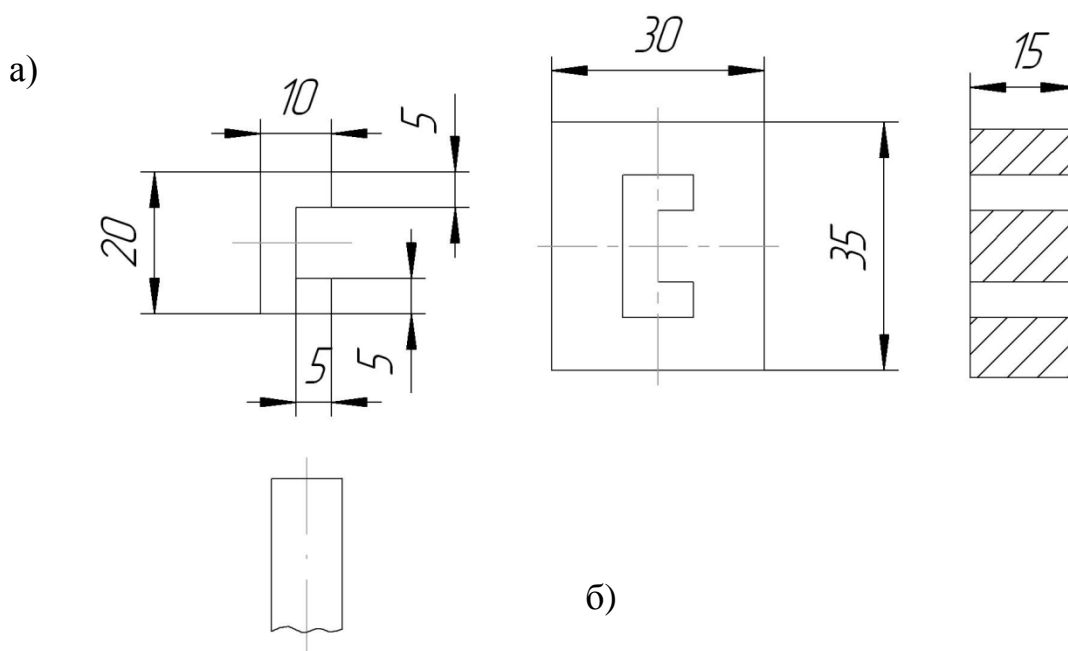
а) – эскиз инструмента; б) – эскиз заготовки.
